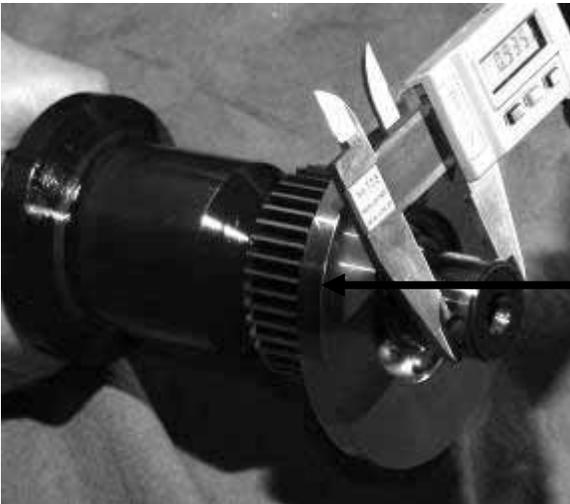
Tolerancias de los Cojinetes, Rodamientos y Ejes.
